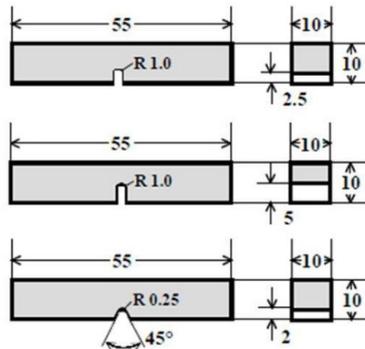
Eprouvettes Charpy standardisées. Le type le plus utilisé est l'éprouvette ISO-V. Dimensions en mm.
